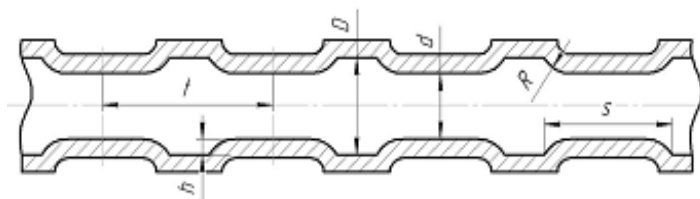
Конструктивная схема предлагаемой сферической углубленной трубы:
